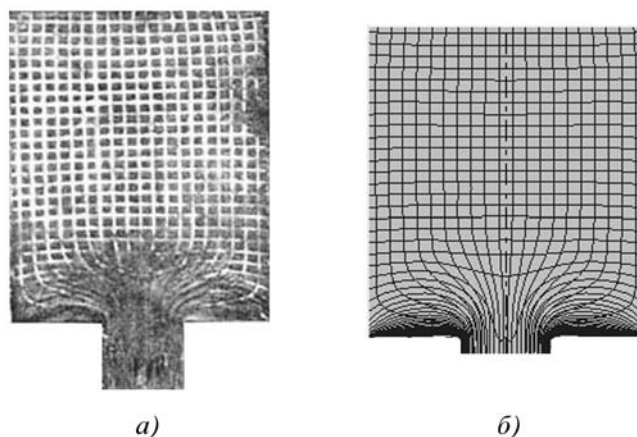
Экспериментальная (а) и расчетная (б) координатные сетки при обратном прессовании без смазки: а – заготовка из свинца; $D_k = 40$ мм; б – заготовка из сплава Д16; $D_k = 110$ мм
